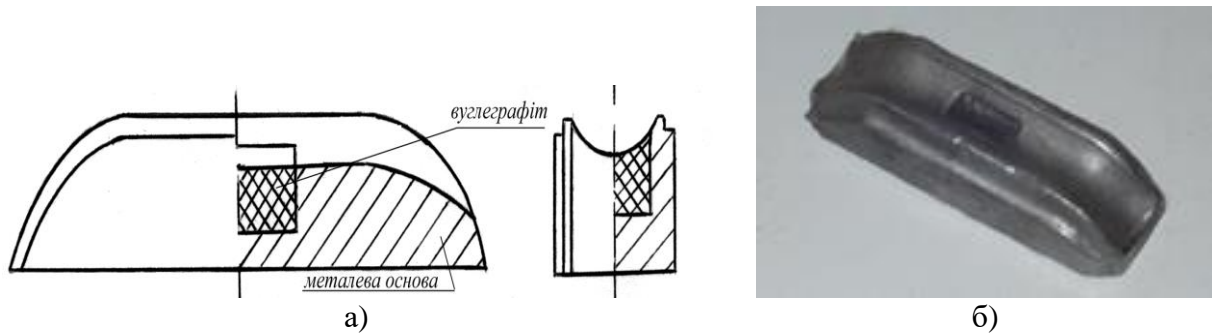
Металева вставка вкладка з вуглеграфітовою для струмознімача (а – конструктивні особливості; б – реальний вигляд)
